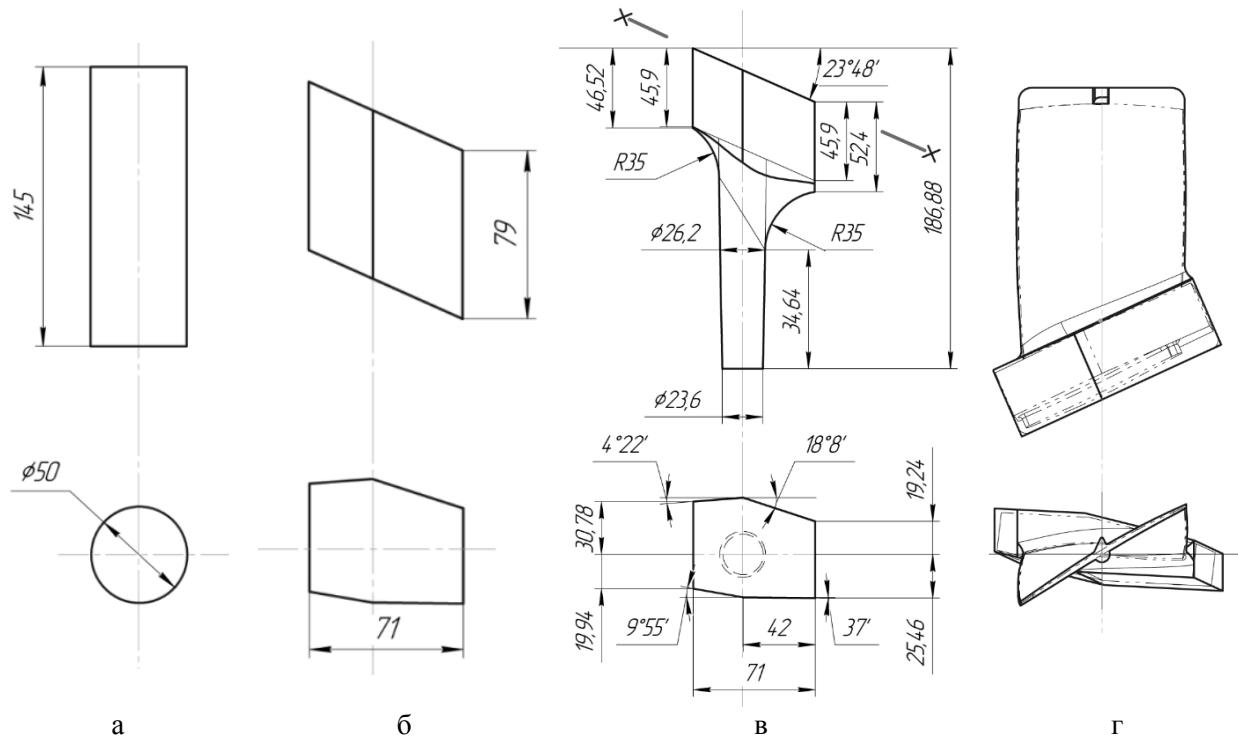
Формы и замеры заготовки по переходам технологической схемы штамповки:
